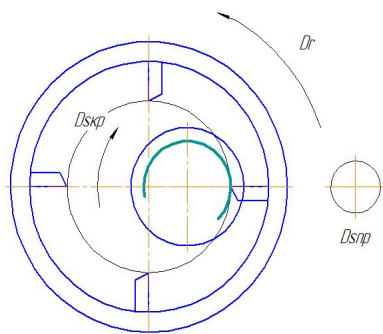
Фрезерование резьбы методом внутреннего касания
